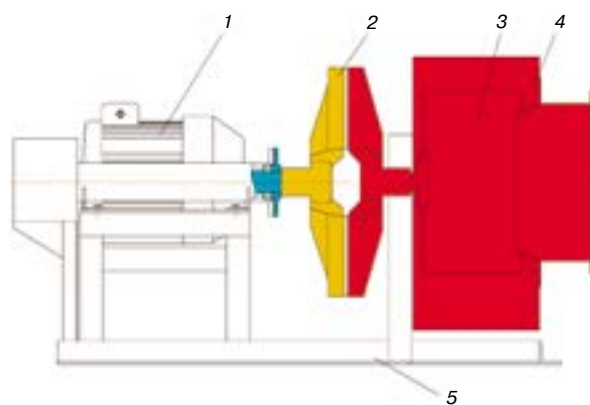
Схема устройства жарового вентилятора «Гелиотис»: 1 – двигатель; 2 – муфта; 3 – крыльчатка; 4 – улитка с воздухозаборником; 5 – рама
